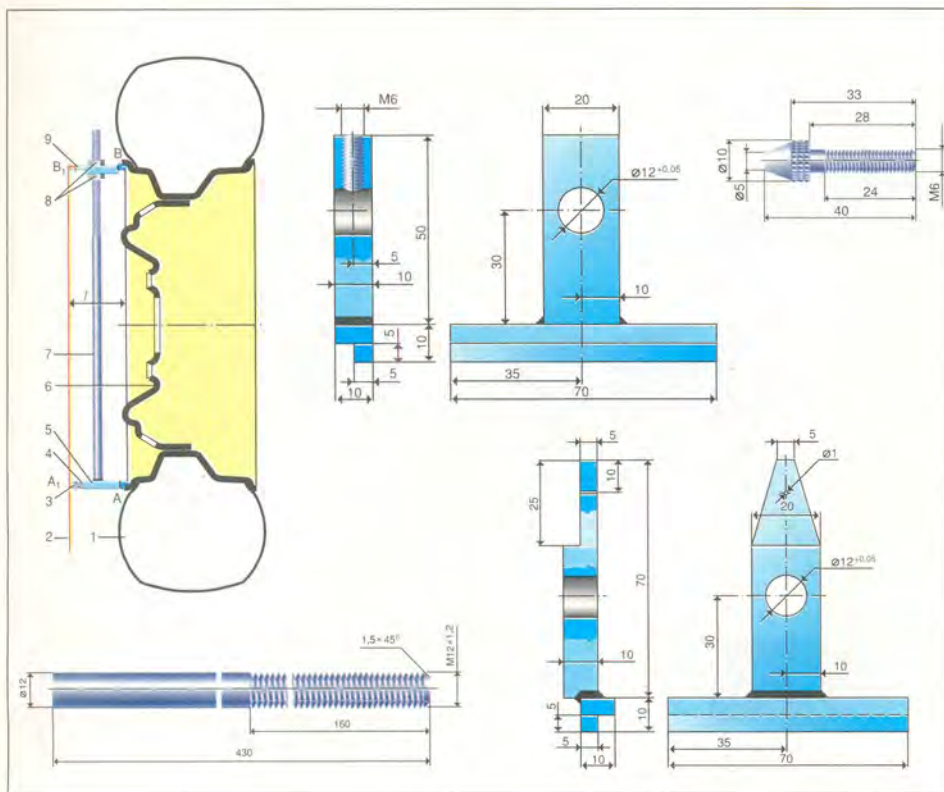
Установка приспособления на колесо: 1 – шина; 2 – нить; 3 – регулировочный винт; 4 – контргайка; 5 – жесткий упор; 6 – обод; 7 – штанга; 8 – гайка; 9 – регулируемый упор; А, В – точки контроля.
